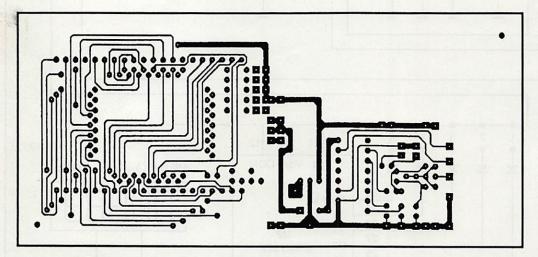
Circuit imprimé double face, trous métallisés, côté soudures.
